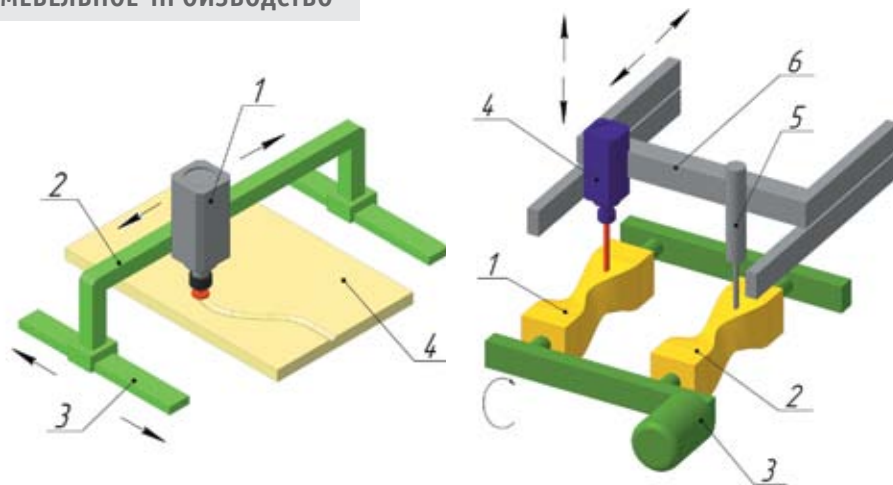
Фрезерный станок для объемного фрезерования с ЧПУ (тип 1):
